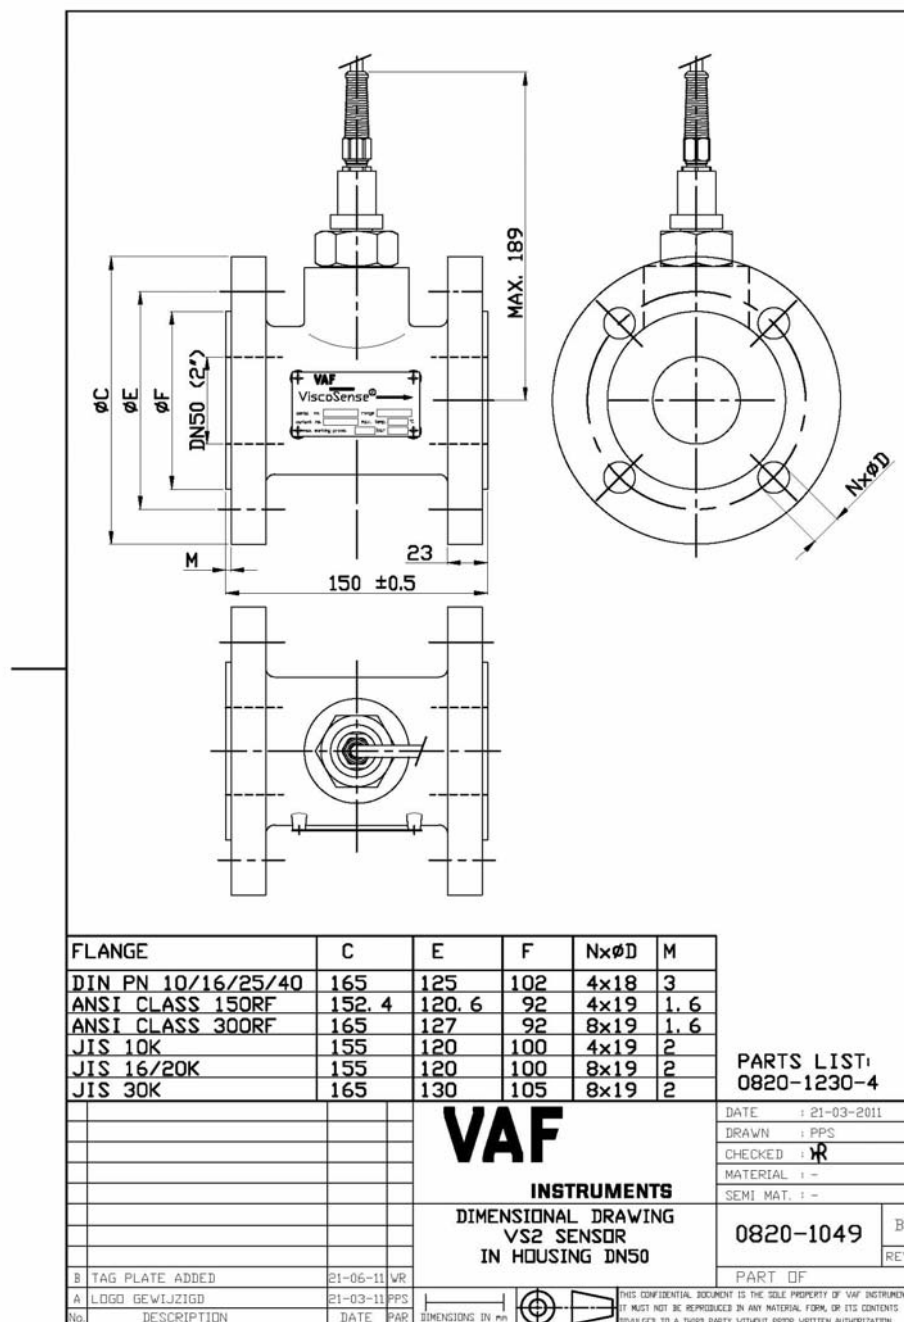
Dimensioni del sensore ViscoSense®2 (Tutte le dimensioni sono in millimetri).
